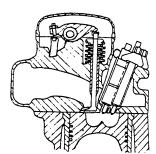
Zylinderkopf des Methanolmotors mit 2 Einspritzdüsen
